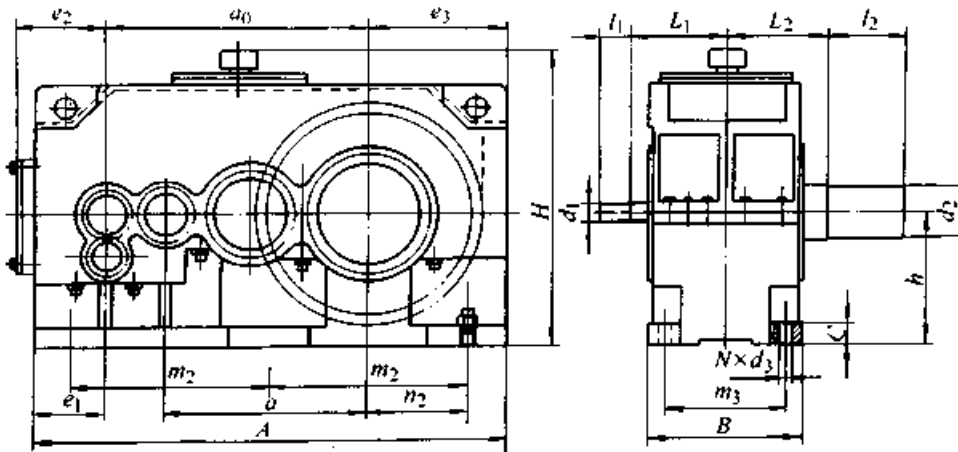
MPR2、MPR3、MPR4 减速器外形尺寸
